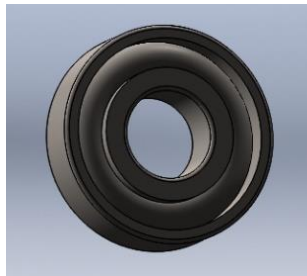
11: RODAMIENTO DE BOLA. FUENTE: AUTOR.
